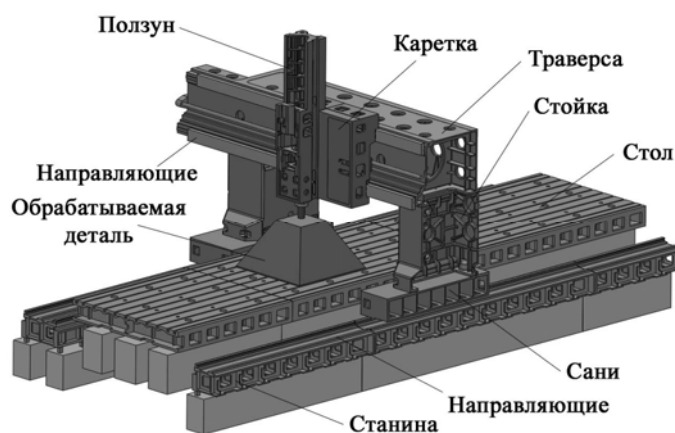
Несущая система продольно-фрезерного станка с подвижным порталом
